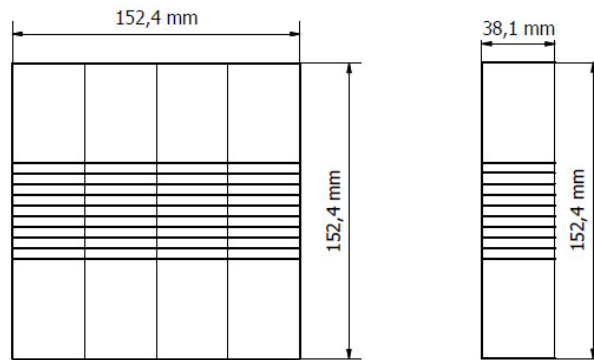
Dimensiones de las probetas para el ensayo de corrosión.
